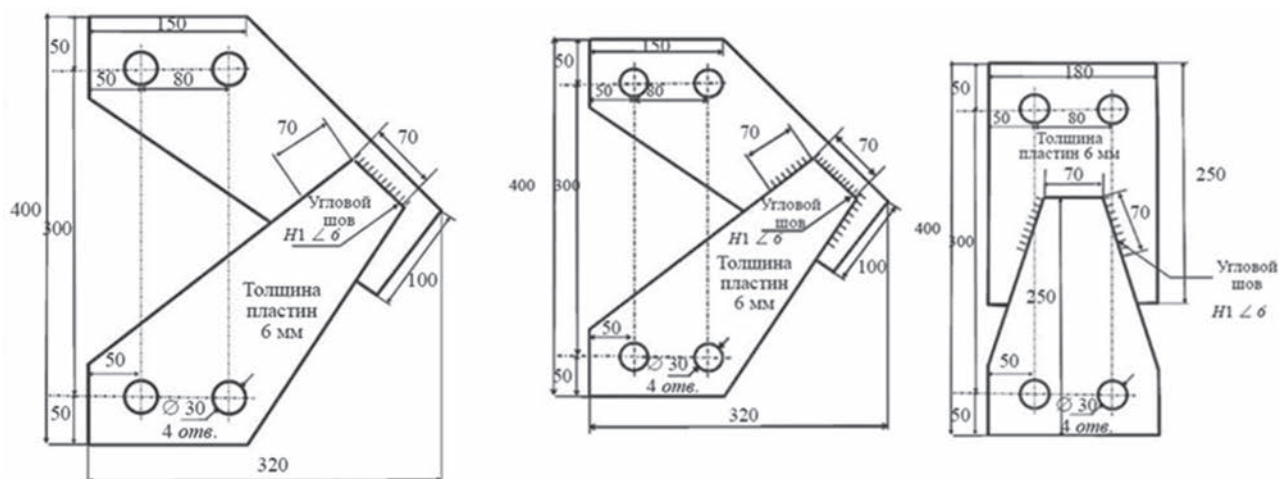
Образцы нахлесточных сварных соединений
